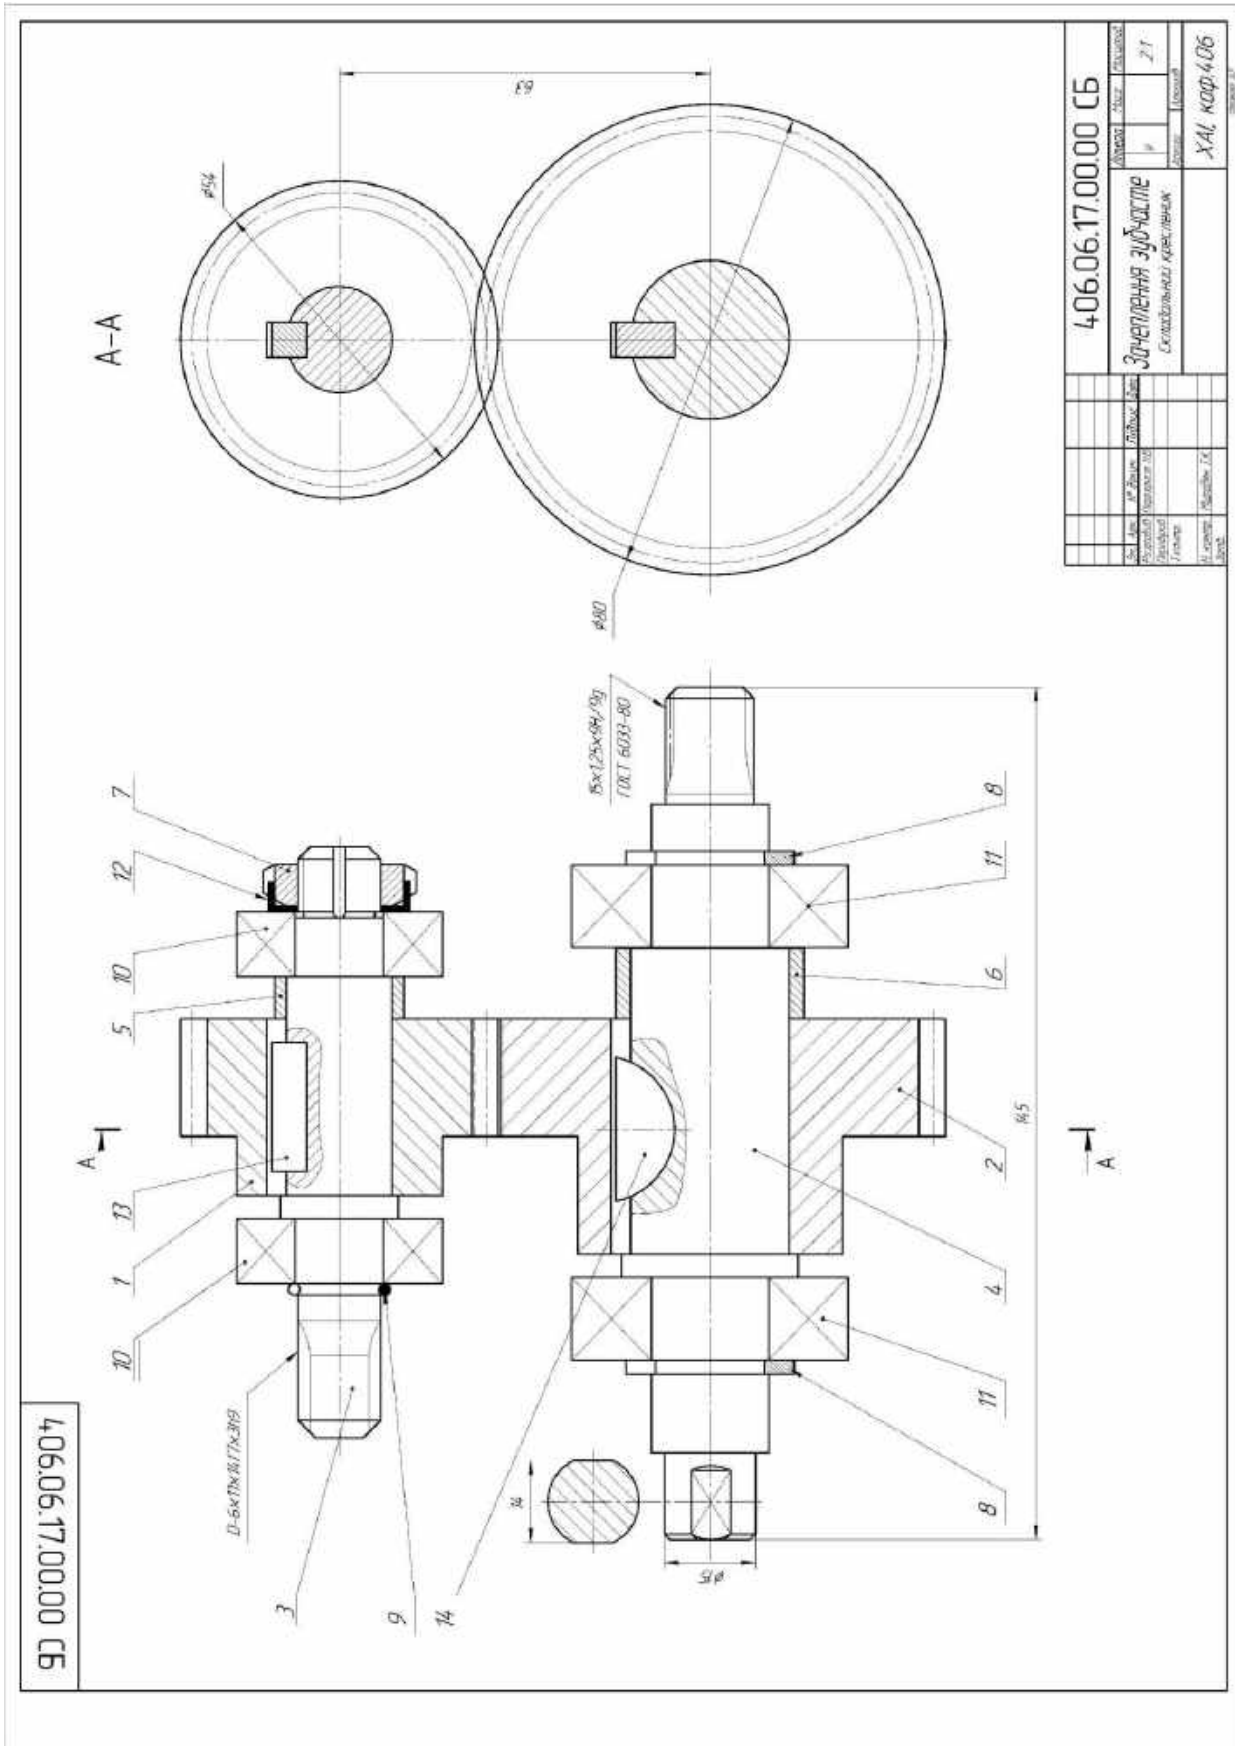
Складальний креслений зубчастого зачеплення з підшипниками
